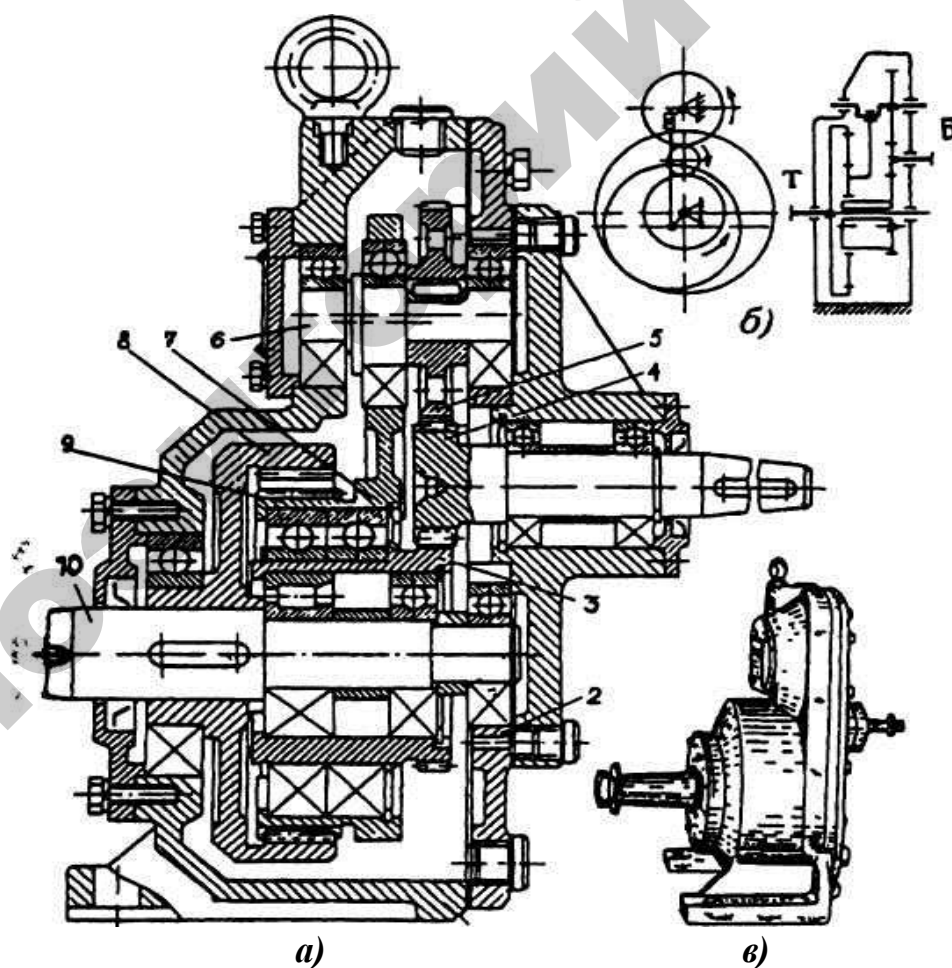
Цилиндрический колесно-шатунный редуктор:
